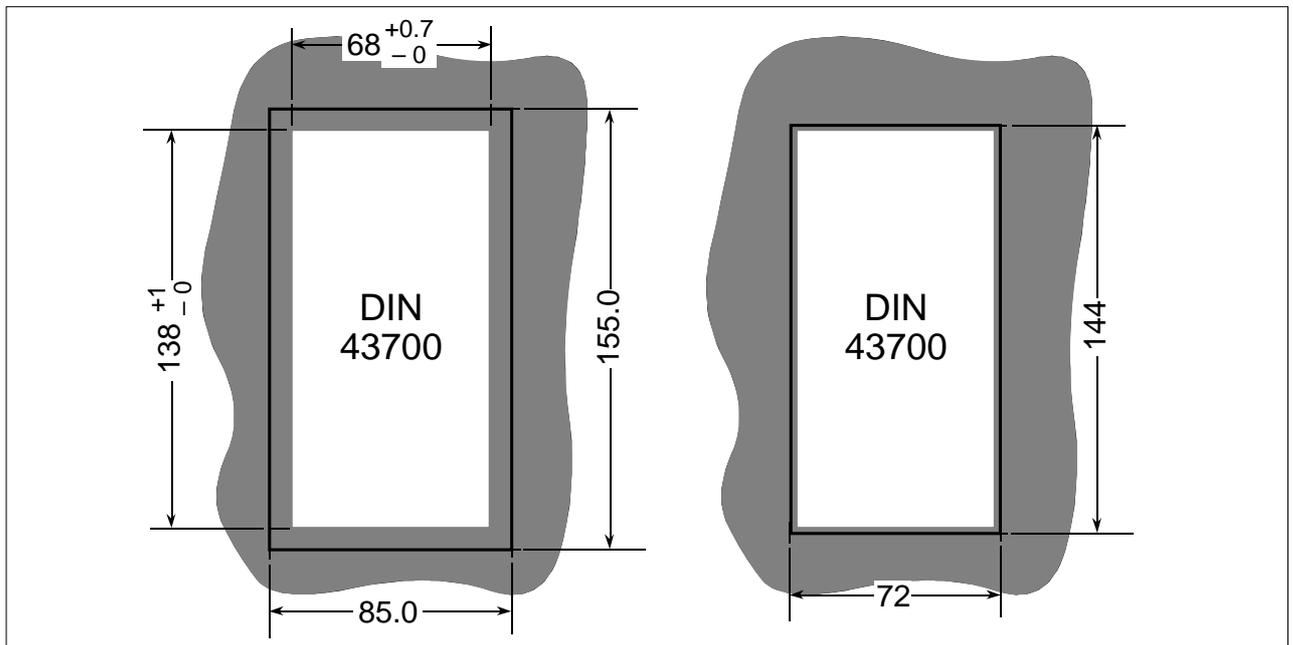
Dimensioni del pannello di copertura— IP65 (sin.) & non-IP65 (destra)
